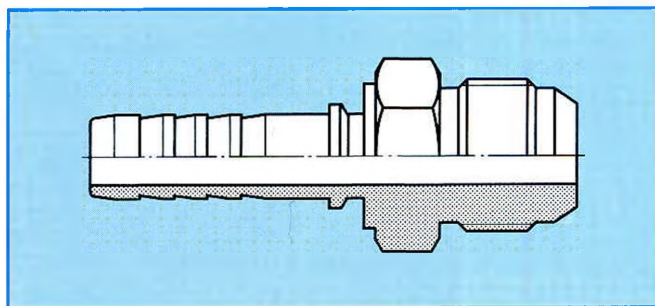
Прямой ниппель с наружной резьбой для резьбового соединения с уплотняющей отбортовкой
